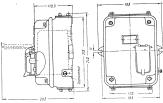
Габаритные и установочные размеры автомати-типа АП25 в чугунном корпусе
